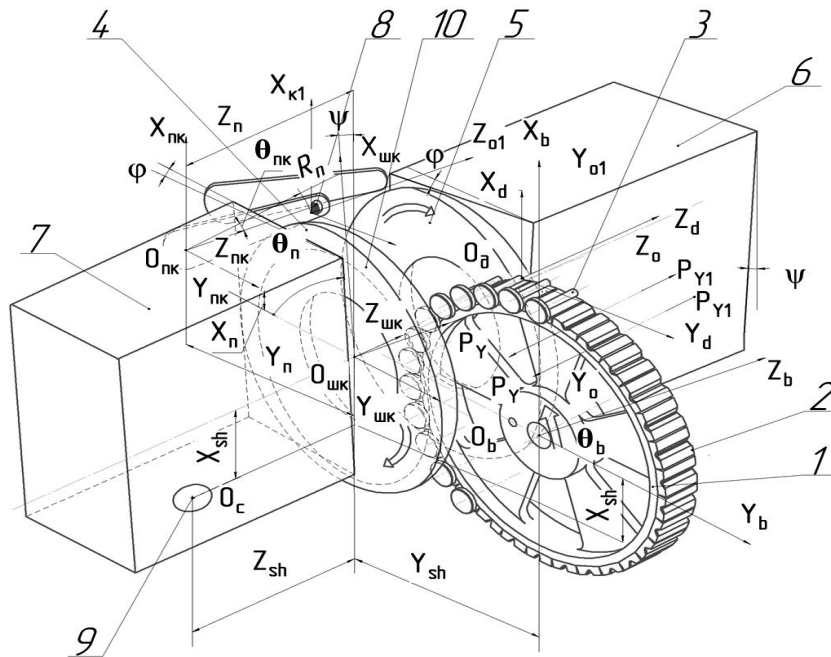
Розрахункова схема шліфування торців різних діаметрів: 1 – барабан подач виробів, 2 – призма, 3 – заготовка, 4, 5 – шліфувальні круги, 6, 7 – шліфувальні бабки, 8 – пристрій для правки торцевих ділянок шліфувальних кругів, 9 – сферичний шарнір, відносно якого відбувається поворот кругів, 10 – калібруюча ділянка шліфувального круга, що обробляє торці більших діаметрів.
